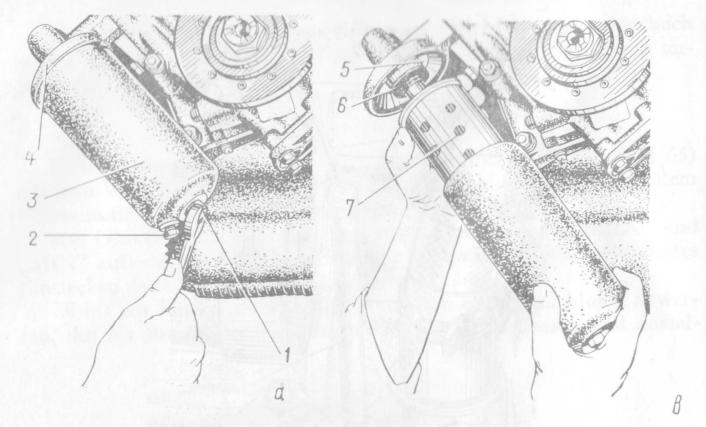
Auswechseln des Filtereinsatzes der Motorschmieranlage:
